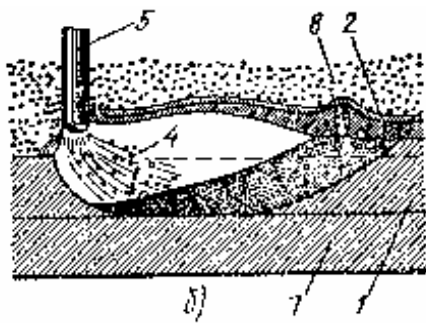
Автоматическая дуговая сварка под флюсом
